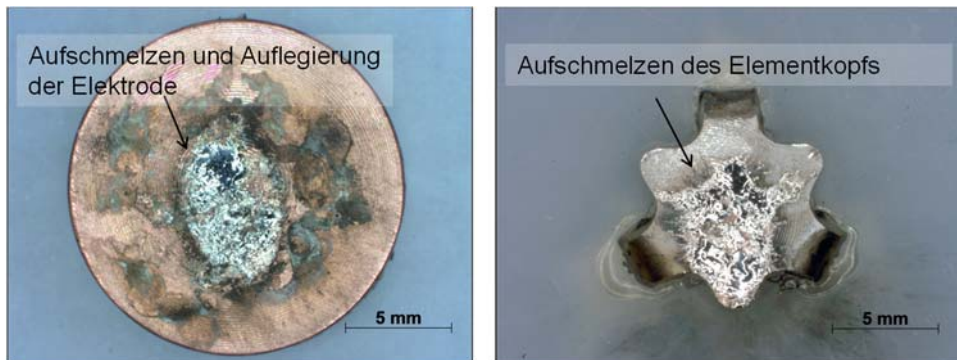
Kontaktoberfläche der Schweißelektrode mit Auflegierung (links). Ein geschweißtes Element (rechts)
